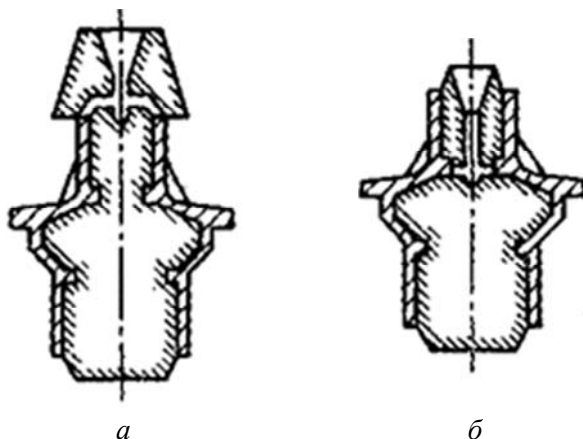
Схемы литниковых систем для заливки сверху (*а*) и сбоку (*б*) через формообразующий песчаный стержень
